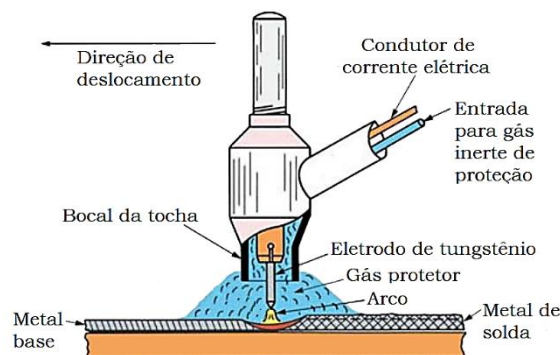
4 – Esquema do processo de soldagem TIG. [Adaptado de AWS, 2001].
